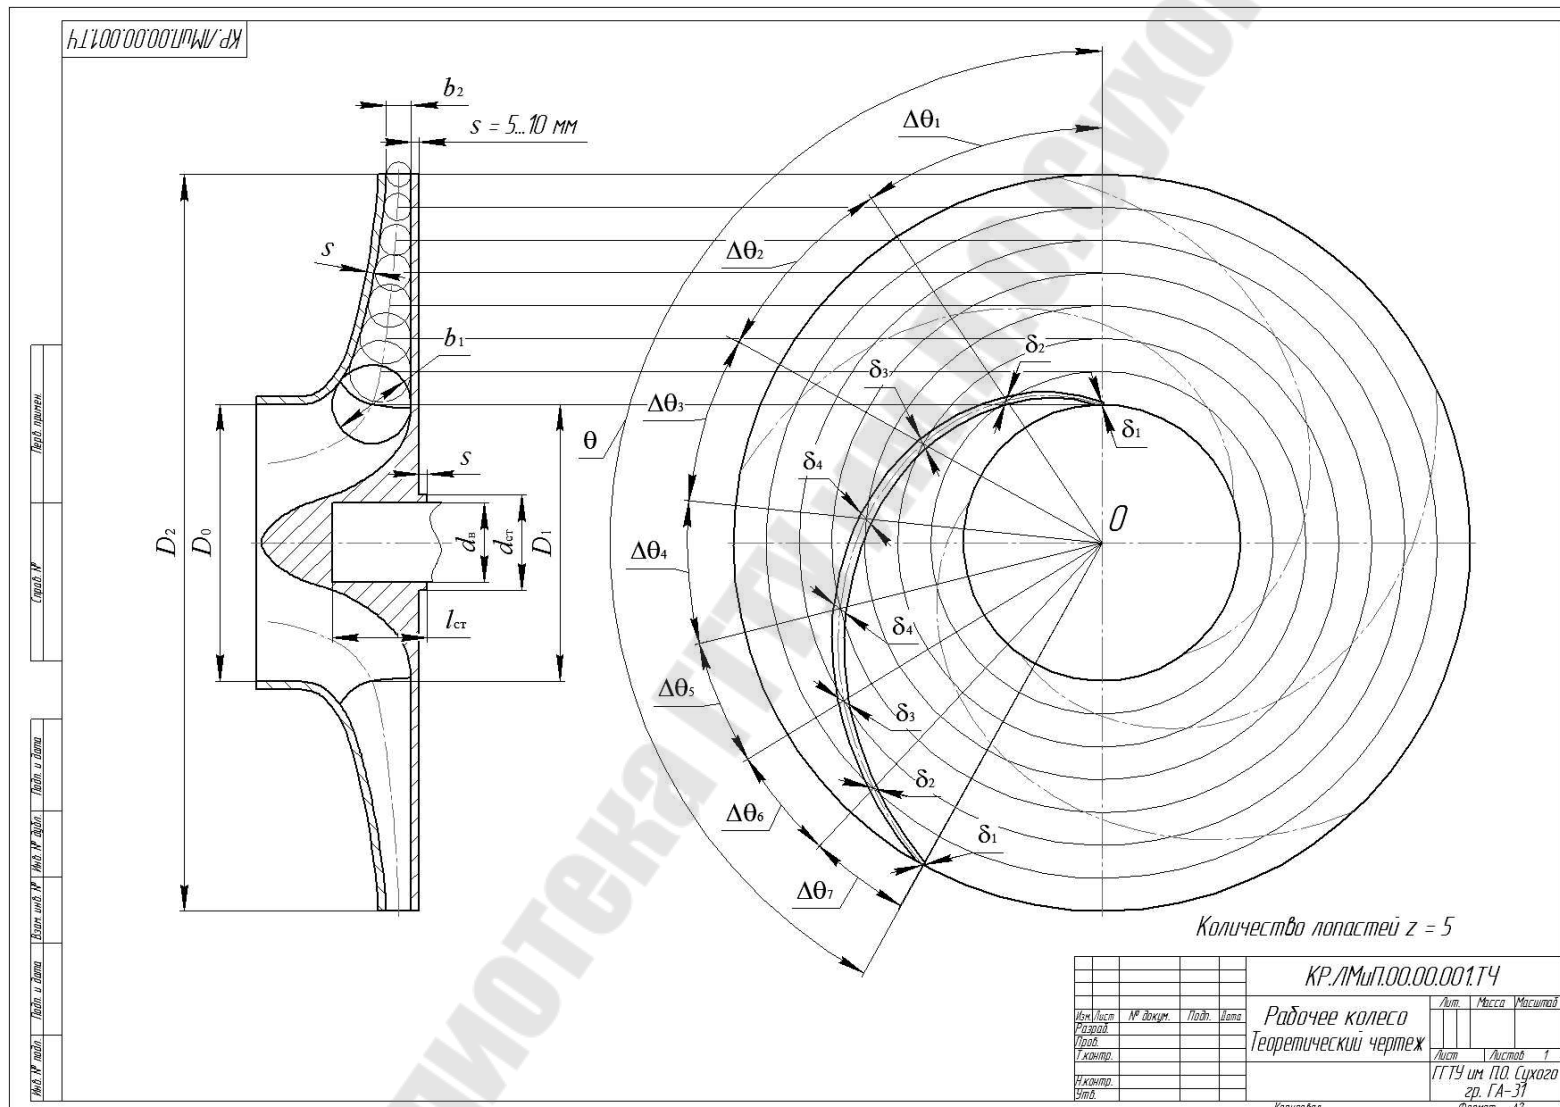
Пример выполнения чертежа рабочего колеса
